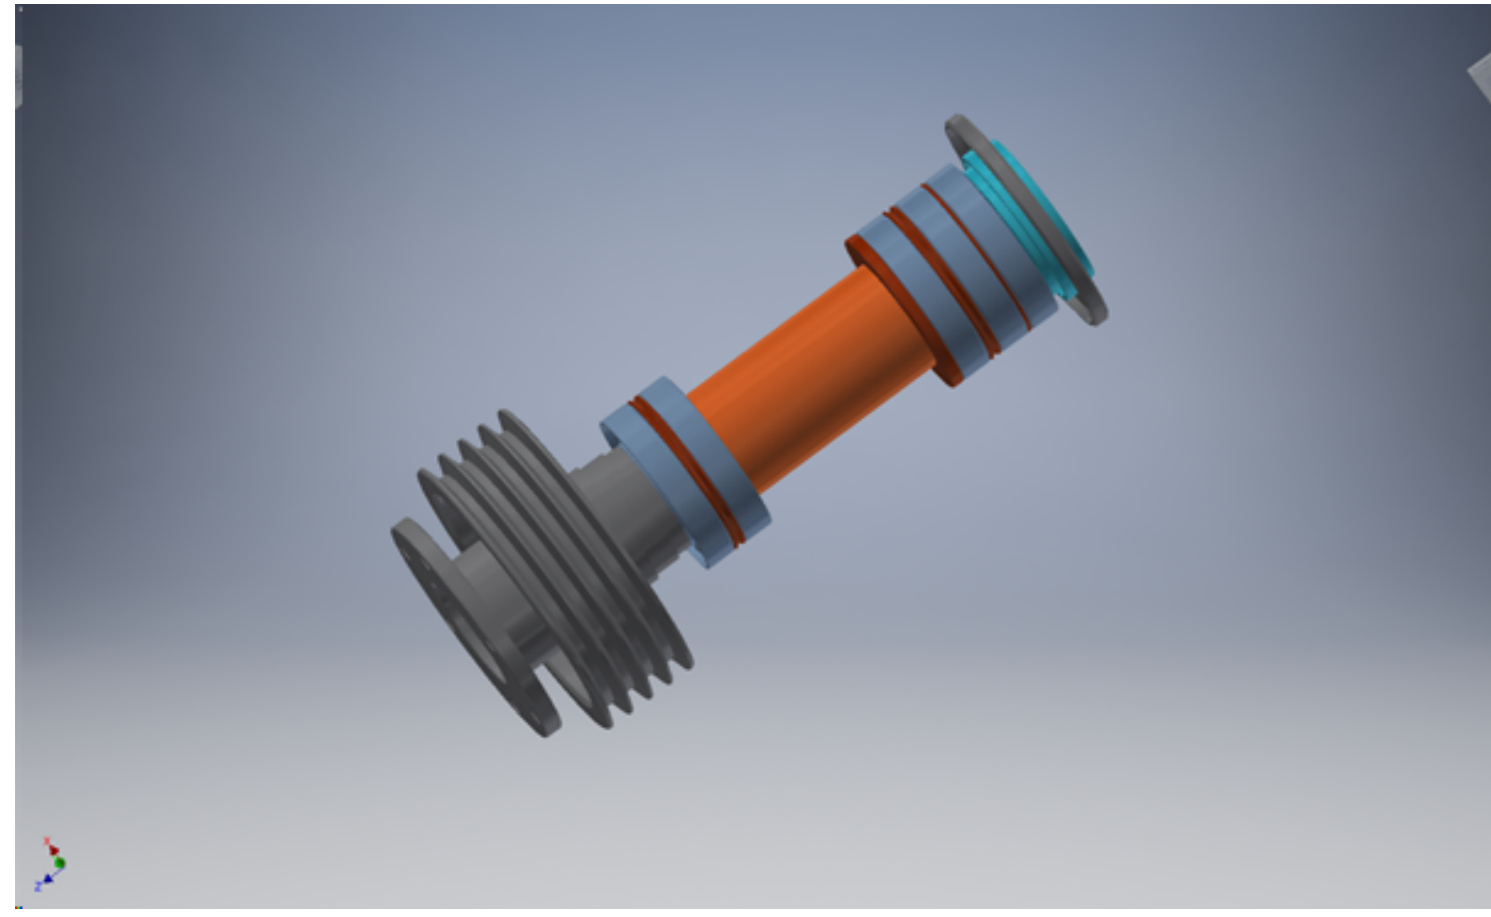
Модель шпинделя токарного верстата ПАБ-130
